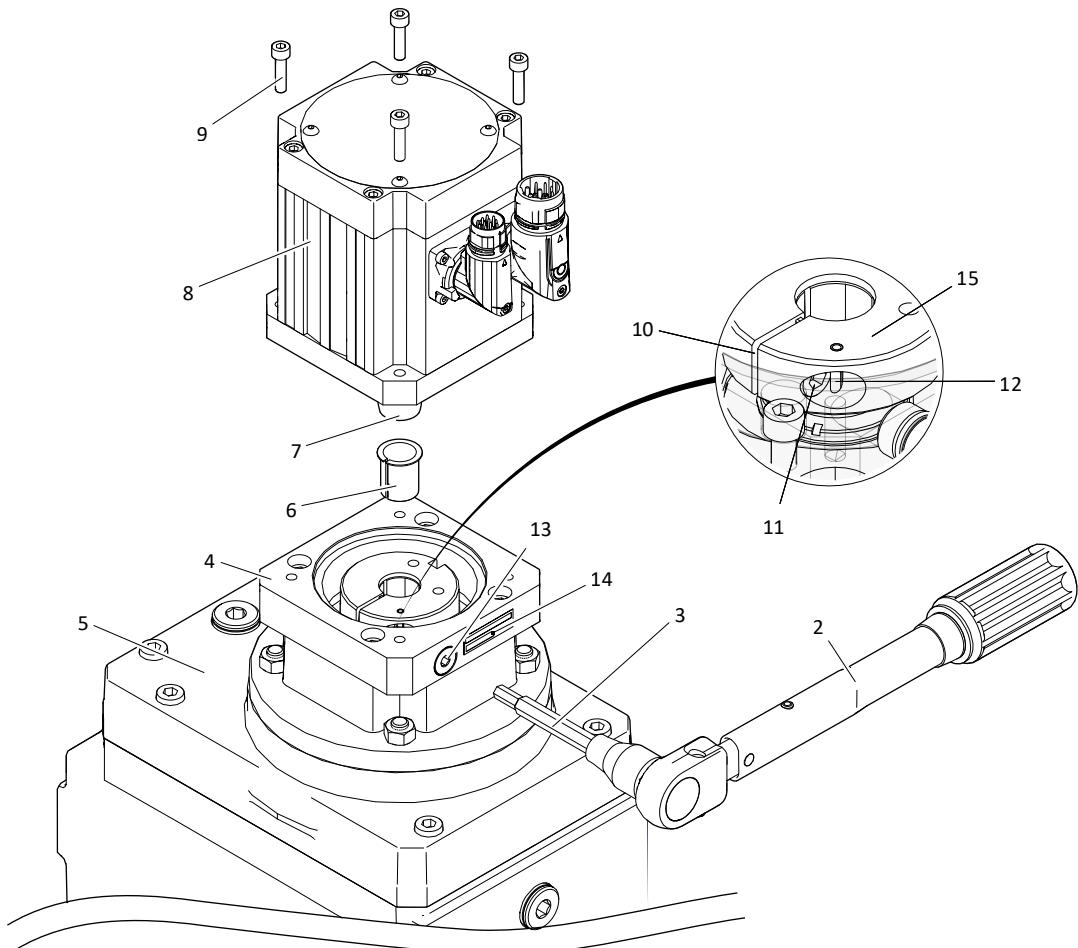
Montaje de un motor en un reductor K con adaptador de motor ME (ejemplo)
